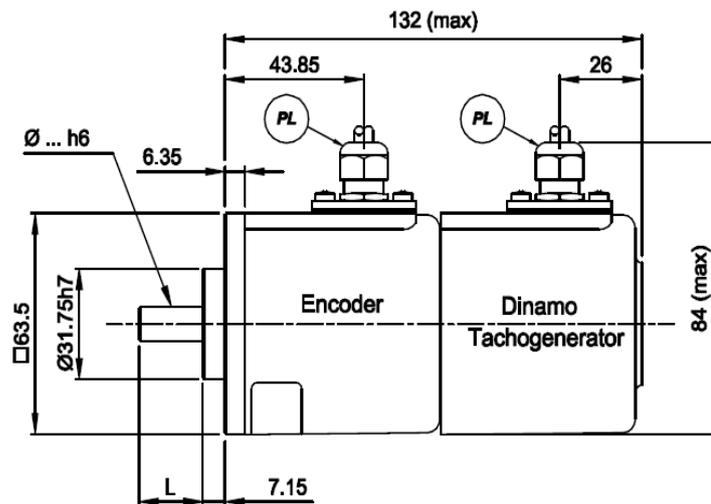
Disegno tecnico encoder con tachogenerator [16]
